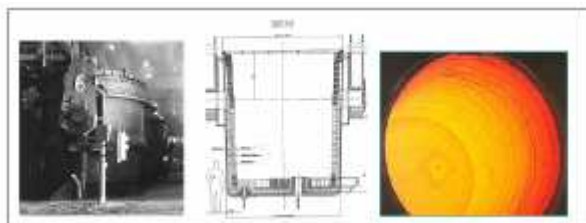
Poche à acier : toilerie, plan de maçonnerie et revêtement réfractaire
